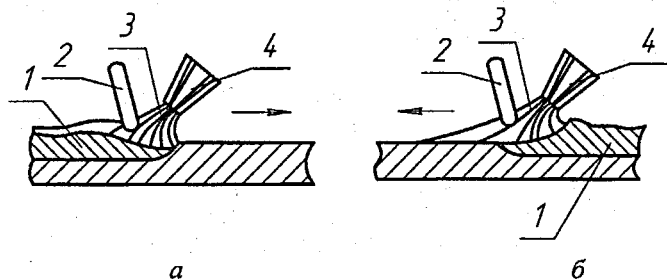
Основні способи газового зварювання: *a* – правий, *б* – лівий; 1 - формуючий шов, 2 - присадний пруток, 3 – полум'я пальника, 4 – пальник
